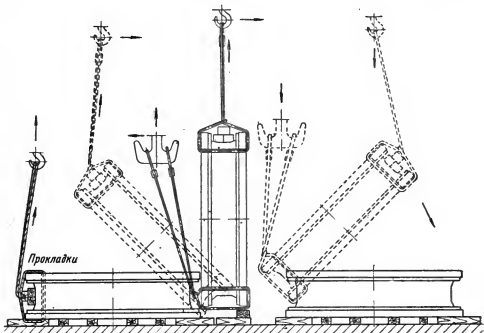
Схема кантовки цилиндрической детали двумя кранами.
